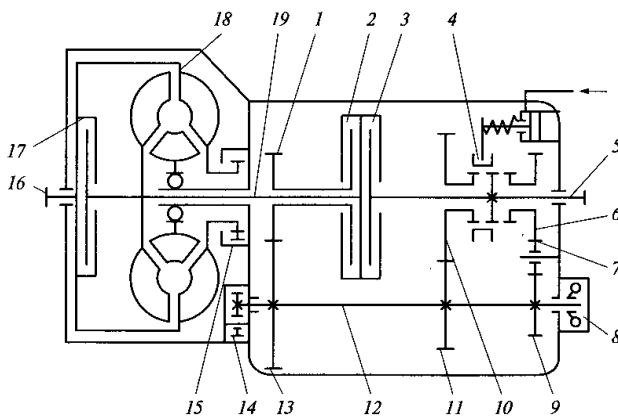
Схема гидромеханической коробки передач:
